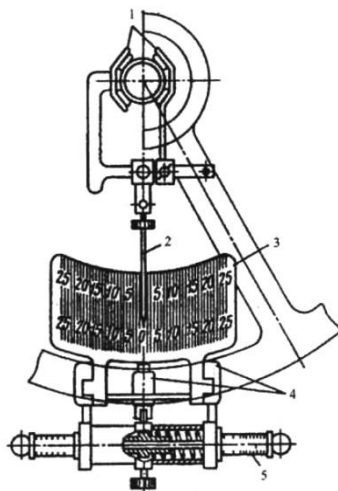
Прилад К-402 для перевірки рульового керування: 1,4 – захвати; 2 – стрілка; 3 – шкала вимірювання люфту; 5 – шкала вимірювання зусилля повороту кермового колеса (динамометра)
